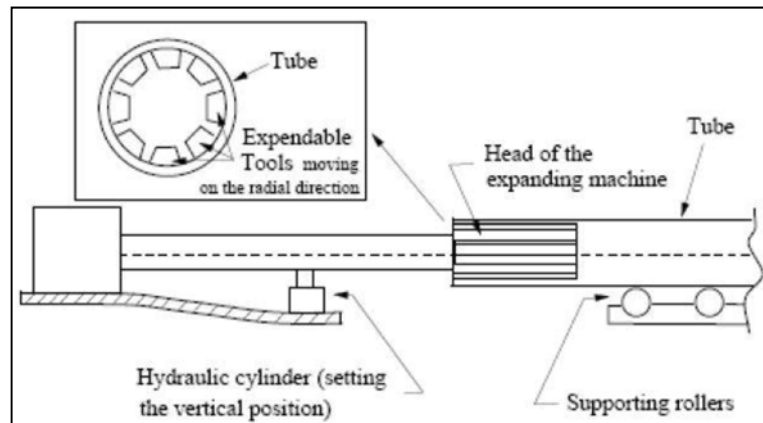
Soudage et finition des tubes par le procédé « UOE » [1].
